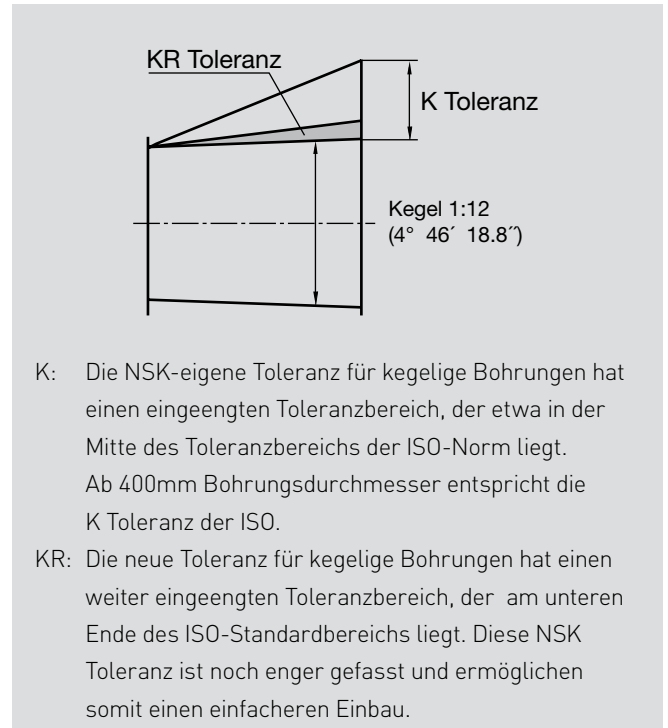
Toleranzen einer kegeligen Bohrung
